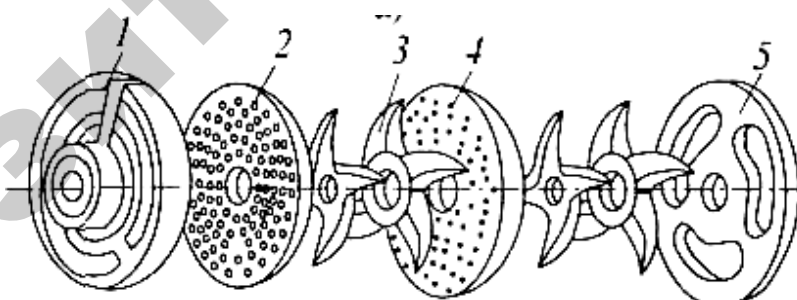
Режущий механизм волчка К7-ФВП-160-2:
